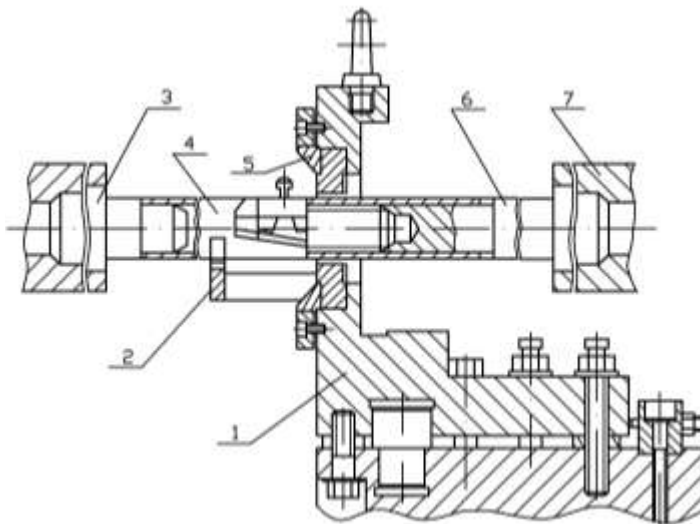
Плаваюча головка для оброблення довгомірних заготовок
